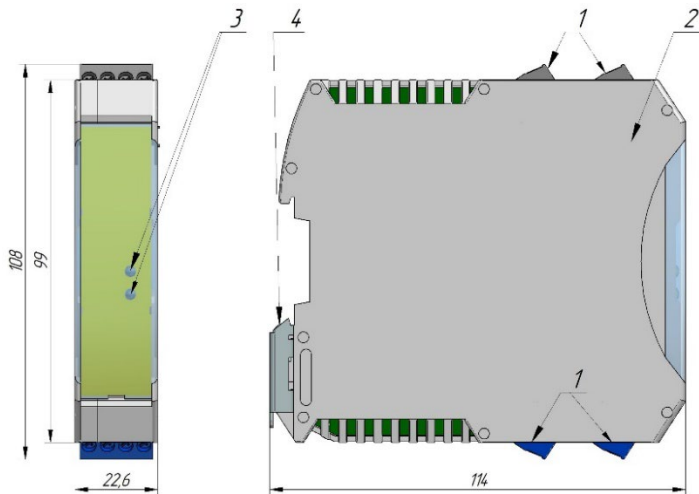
Внешний вид и габаритные размеры МРБ
